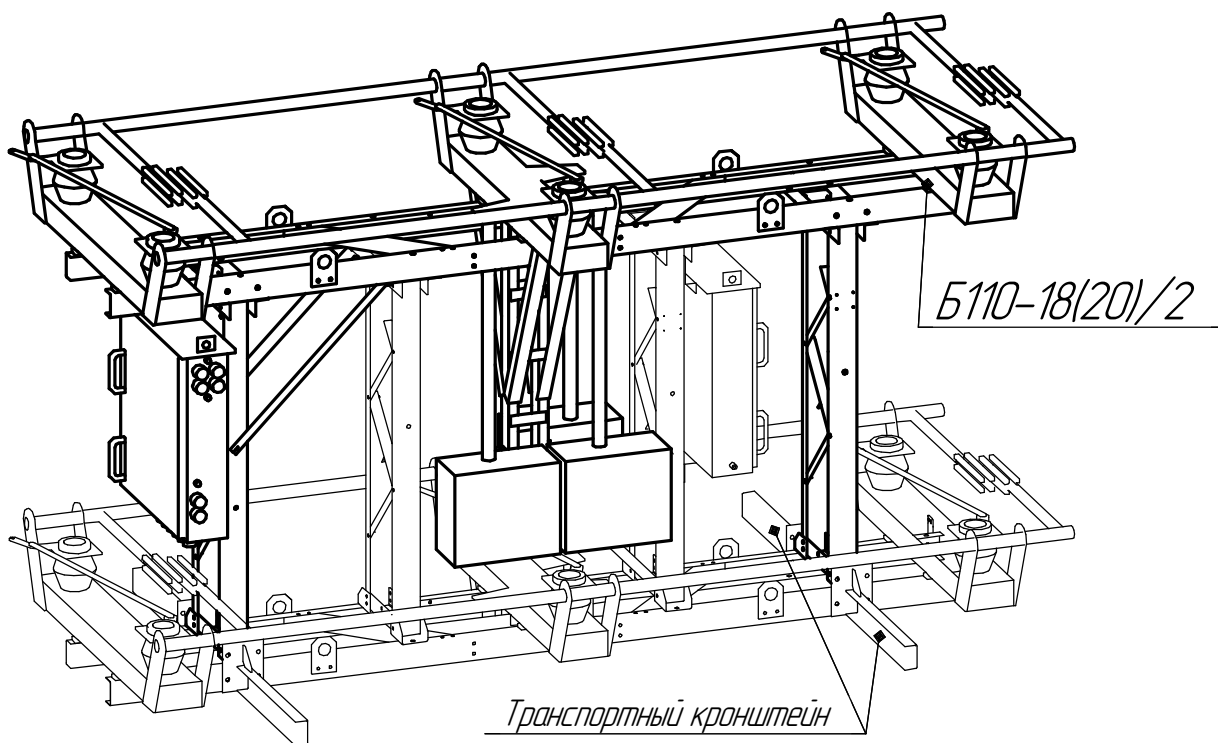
Вид транспортного пакета блока Б110-18(20)
